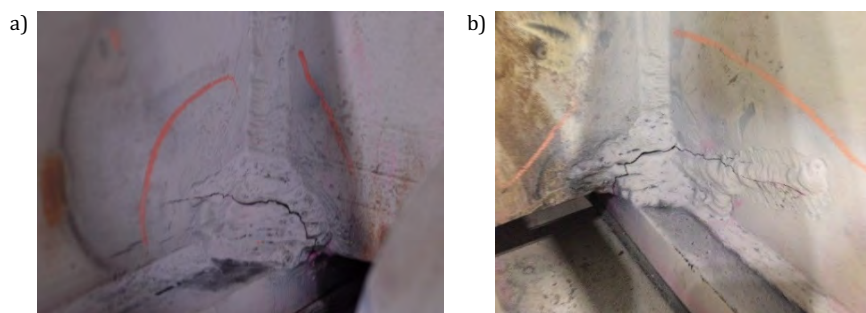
Element konstrukcji zniszczony na skutek zmęczenia cieplnego: a) widok powierzchni; b) przekrój
